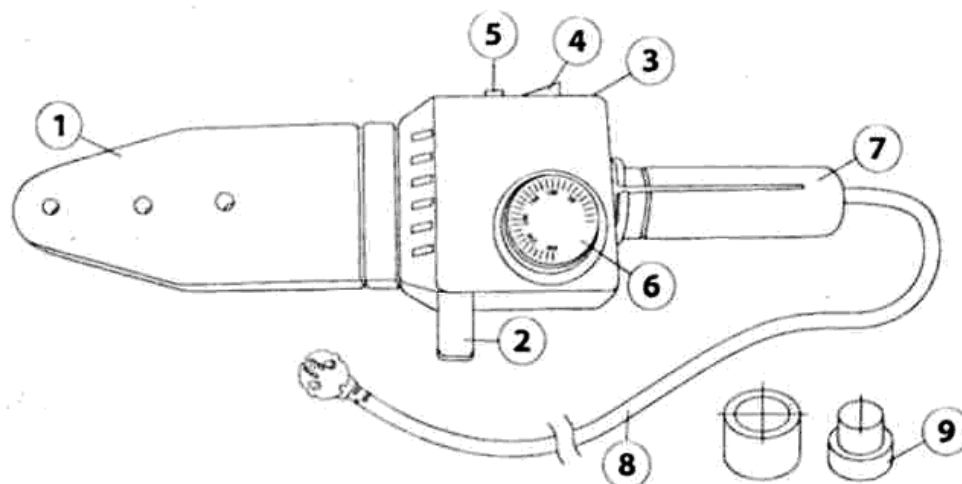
Сварочный аппарат FORAweld-1500-2ST:
